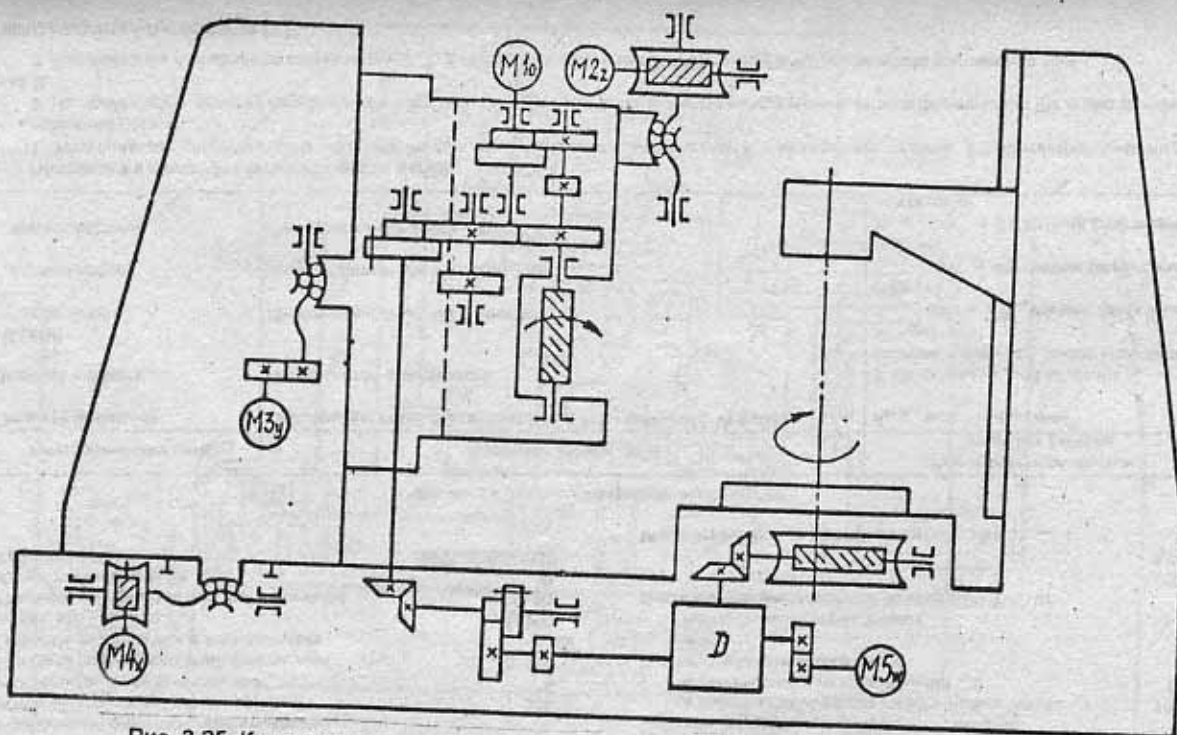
Кинематическая схема зубофрезерного полуавтомата мод. МА 70Ф4 с ЧПУ
